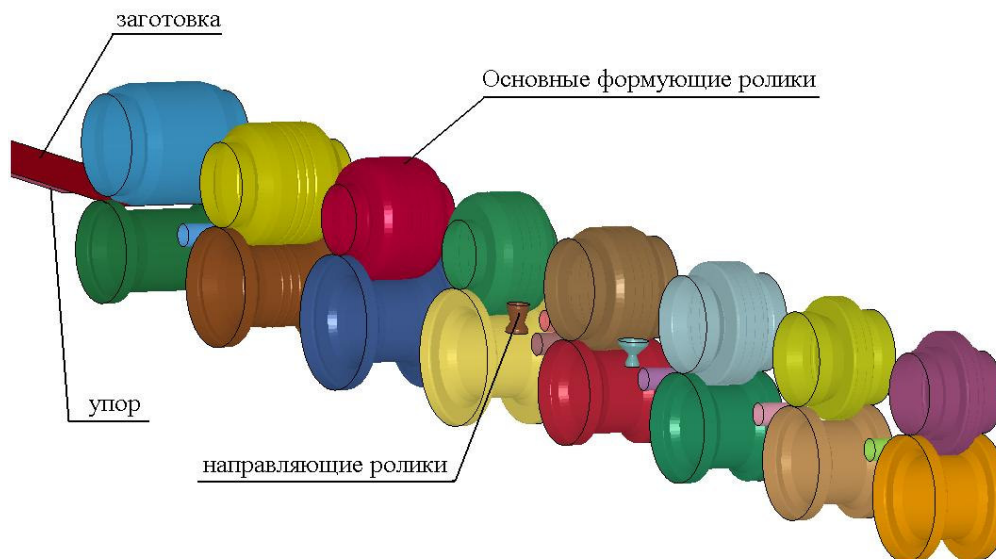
Формообразующая оснастка (8 пар роликовых калибров) для изготовления профиля “Штакетник” 21x70x0,5мм
